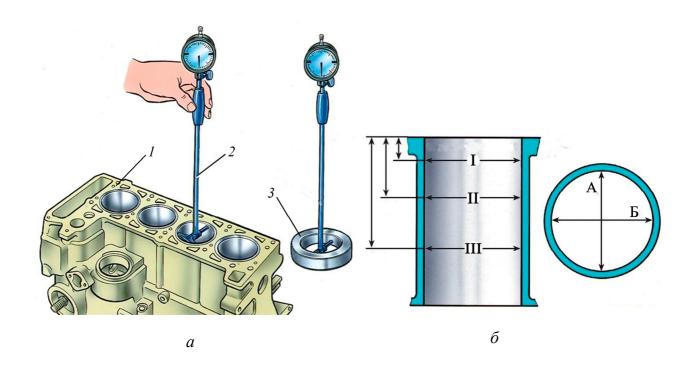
Измерение отверстия цилиндра: 1 – блок цилиндров; 2 – нутромер; 3 – калибр; I, II, III – высота измерения; A, Б – направление измерения
